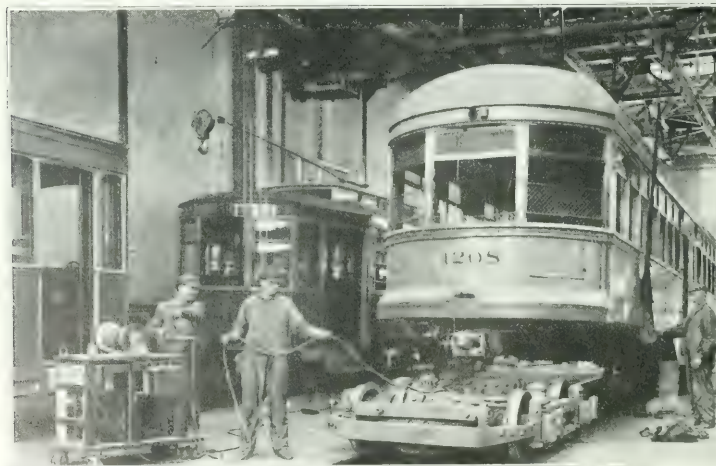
SACANDO UN RODAJE POR SU PROPIO MOTOR
